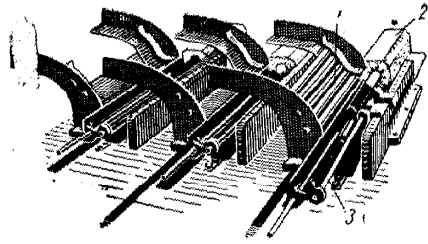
Магазины и индукторы нагревателя фирмы «Асек»:
